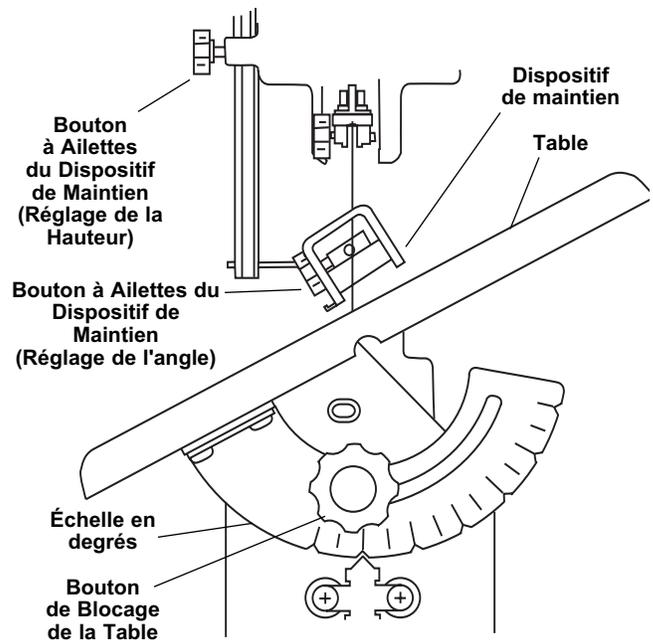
Réglage de la Table pour Sciage Horizontal ou en Biseau
